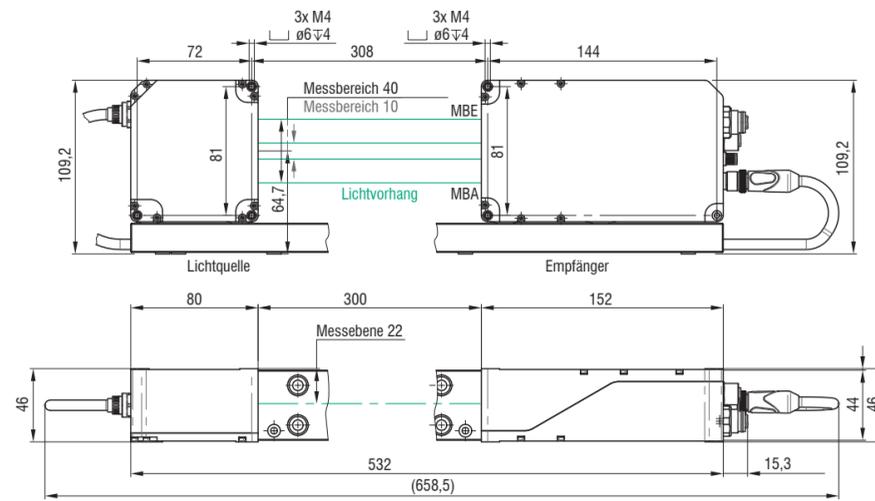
Maßzeichnung Lichtquelle und Empfänger ODC2700-10, ODC2700-40, Abmessungen in mm
